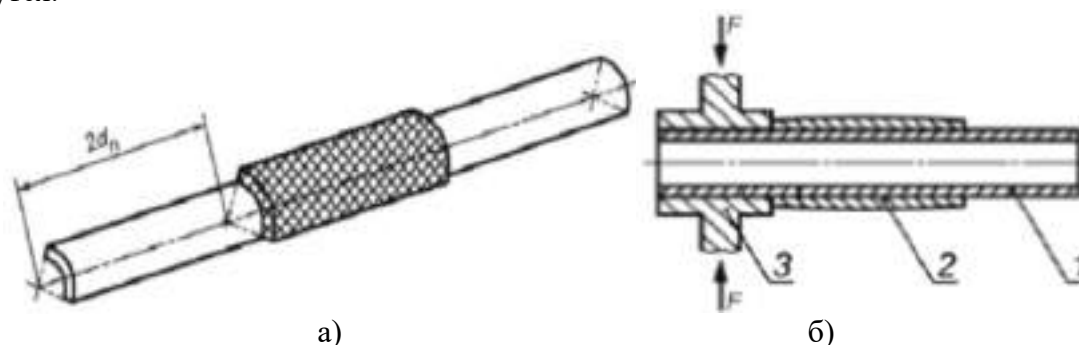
Пример образца (а) и схема проведения испытаний (б) на сплющивание сварного соединения муфтами с закладными нагревателями: 1 – полиэтиленовый трубопровод; 2 – электросварная муфта; 3 – прижимные плиты
